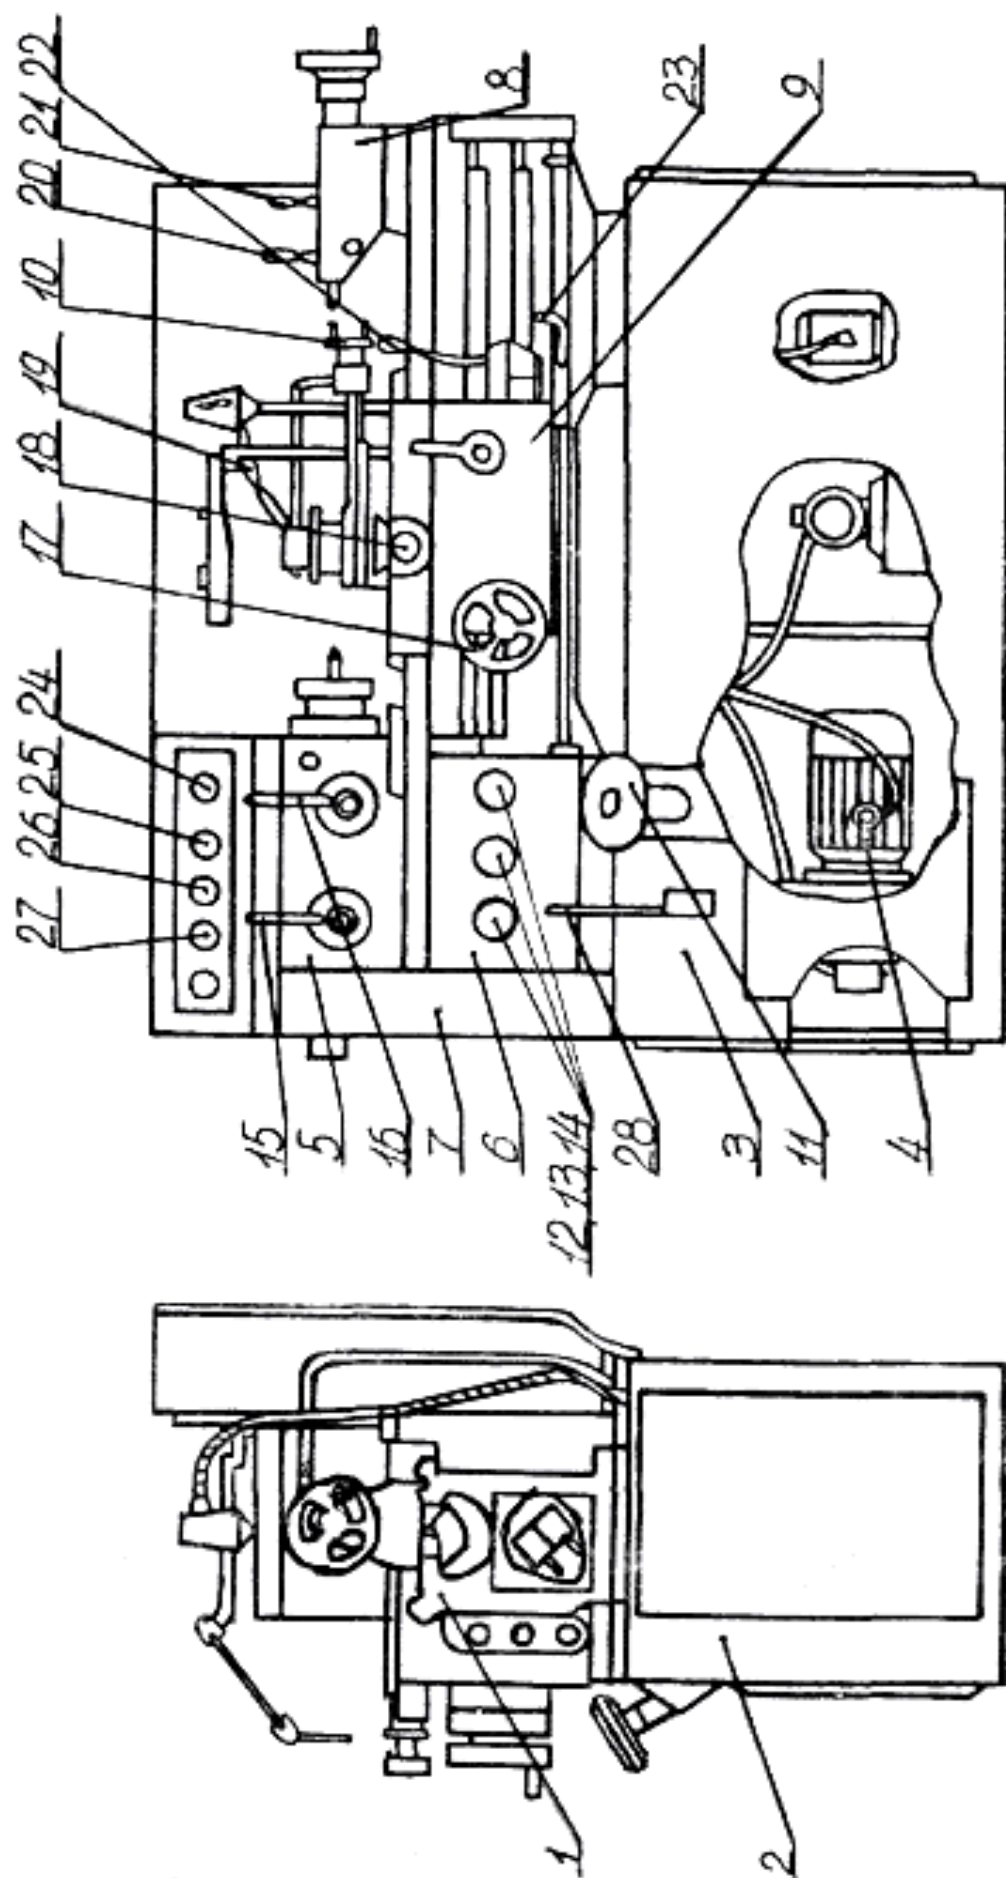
Основные узлы токарно-винтового станка 1ИС611В
